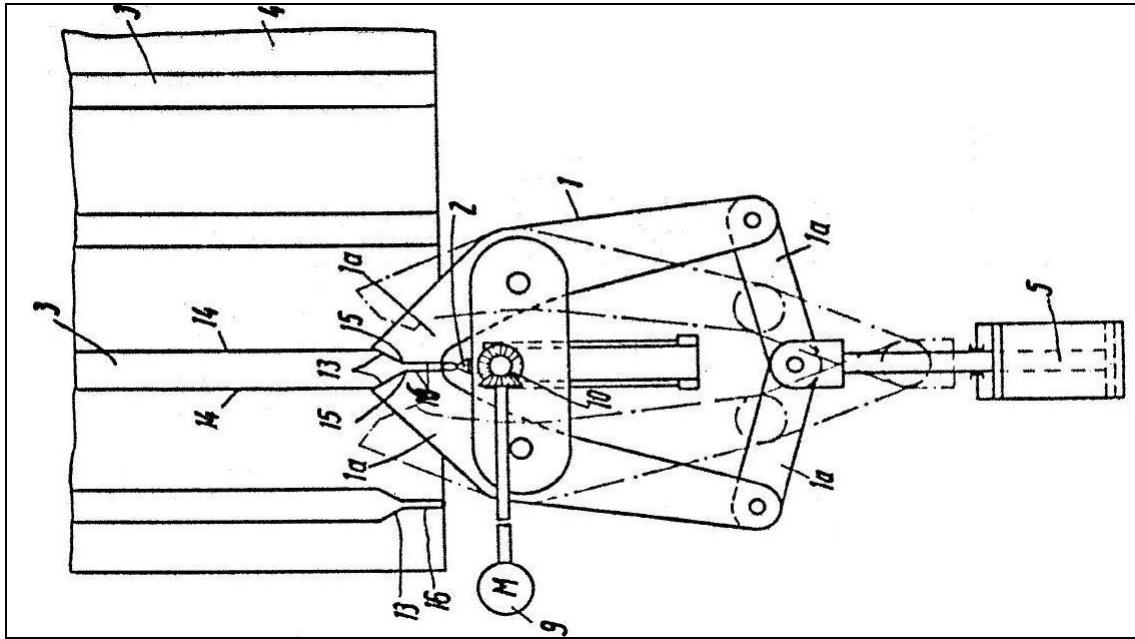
Máquina soldadora de aristas [7]
